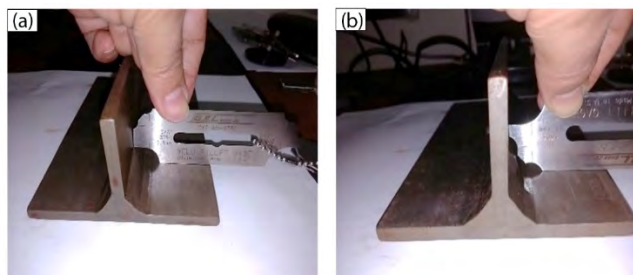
Disposición de Fillet Gauge en juntas en T para verificar el tamaño de pierna en (a) soldadura de filete de cara convexa y (b) soldadura en filete de cara cóncava
